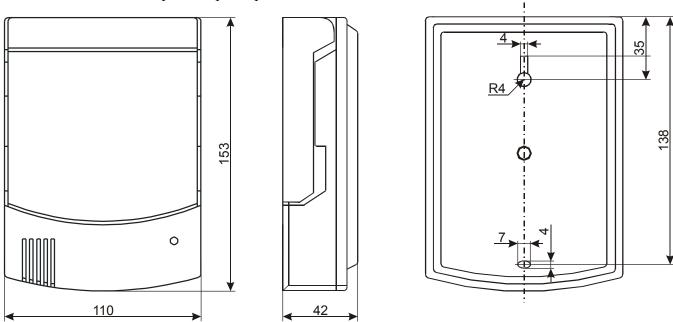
Внешний вид и габаритные размеры ПУО-01
